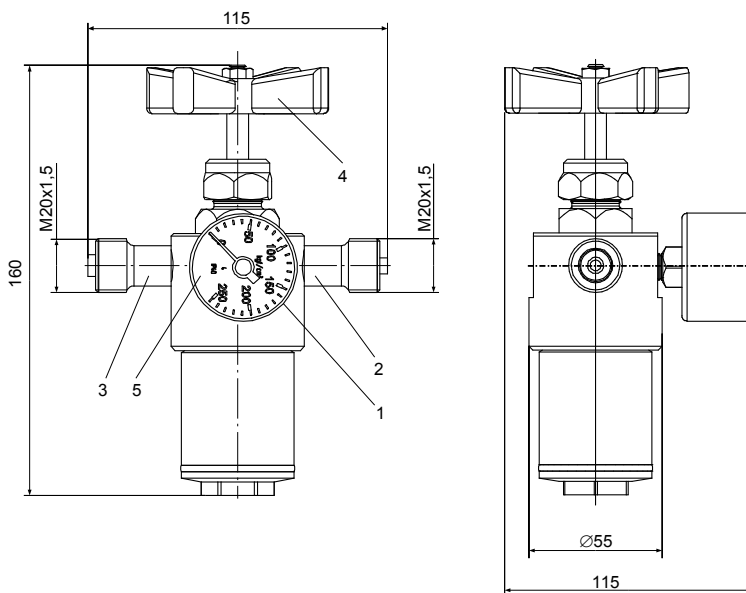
Габаритные и присоединительные размеры ФДУ: 1 – корпус; 2 – штуцер входной; 3 – штуцер выходной; 4 – винт регулировочный; 5 – манометр.
